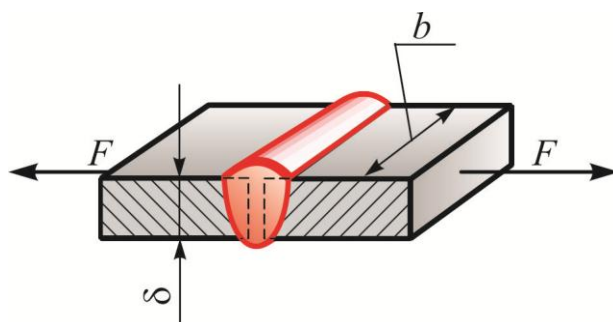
Схема нагружения сварного стыкового соединения растягивающей силой
